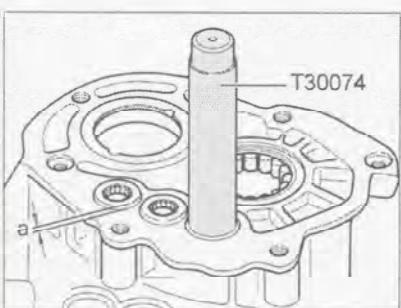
Извлечение и установка шарикоподшипников штоков.
